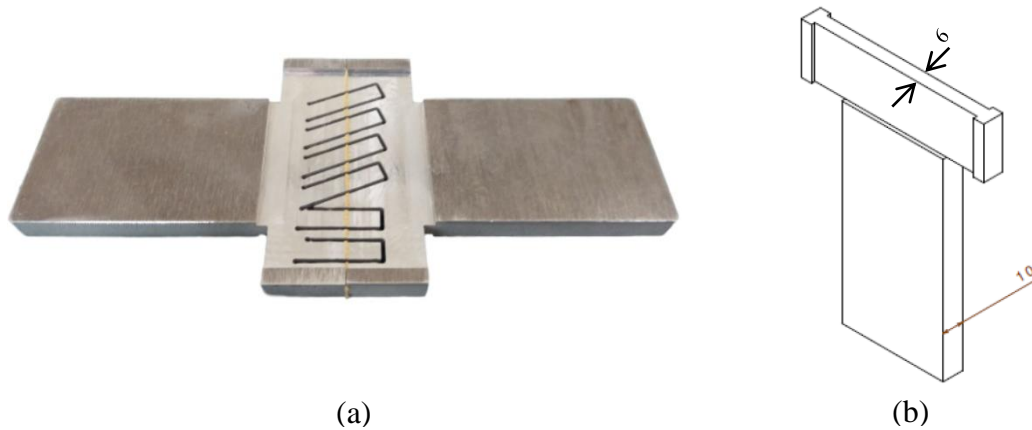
(a) Obtention des éprouvettes mini-Scarf, (b) plan des éprouvettes Scarf modifié sans bec (largeur 6 mm).
